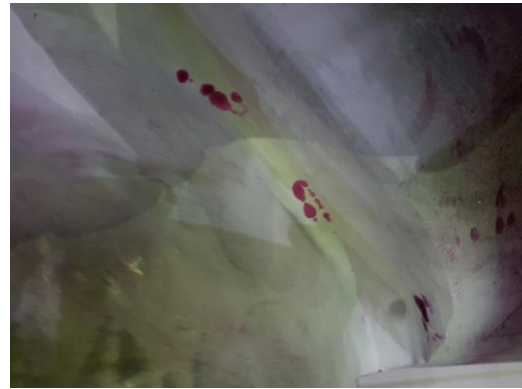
Дефект сварного шва на камере СОД при контроле проникающими веществами
